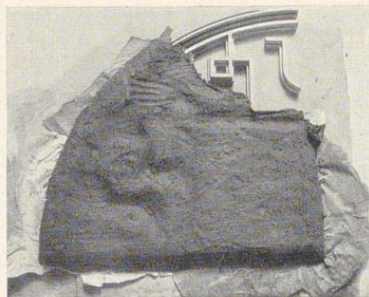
Das Modell für die Schale wird mit Papier und Tonscheiben abgedeckt
